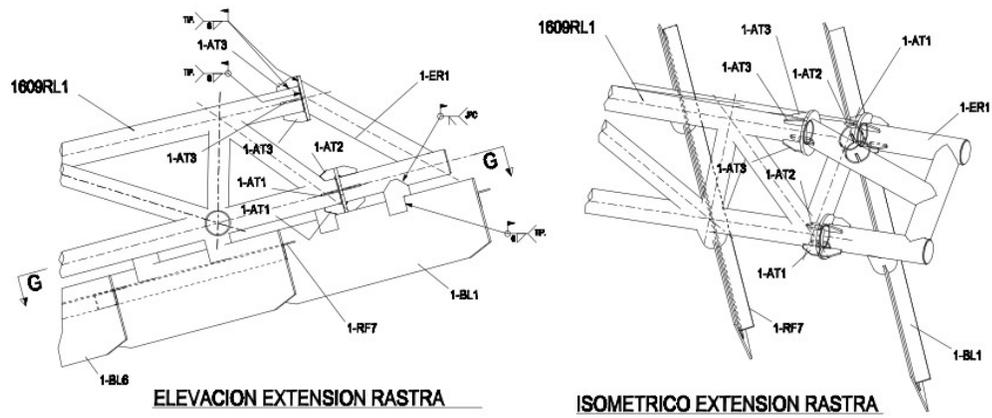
Detalle de Extensión de rastras mediante estructura fabricada. Tomado de «Planos de montaje Modificación de Rastras» (13)
